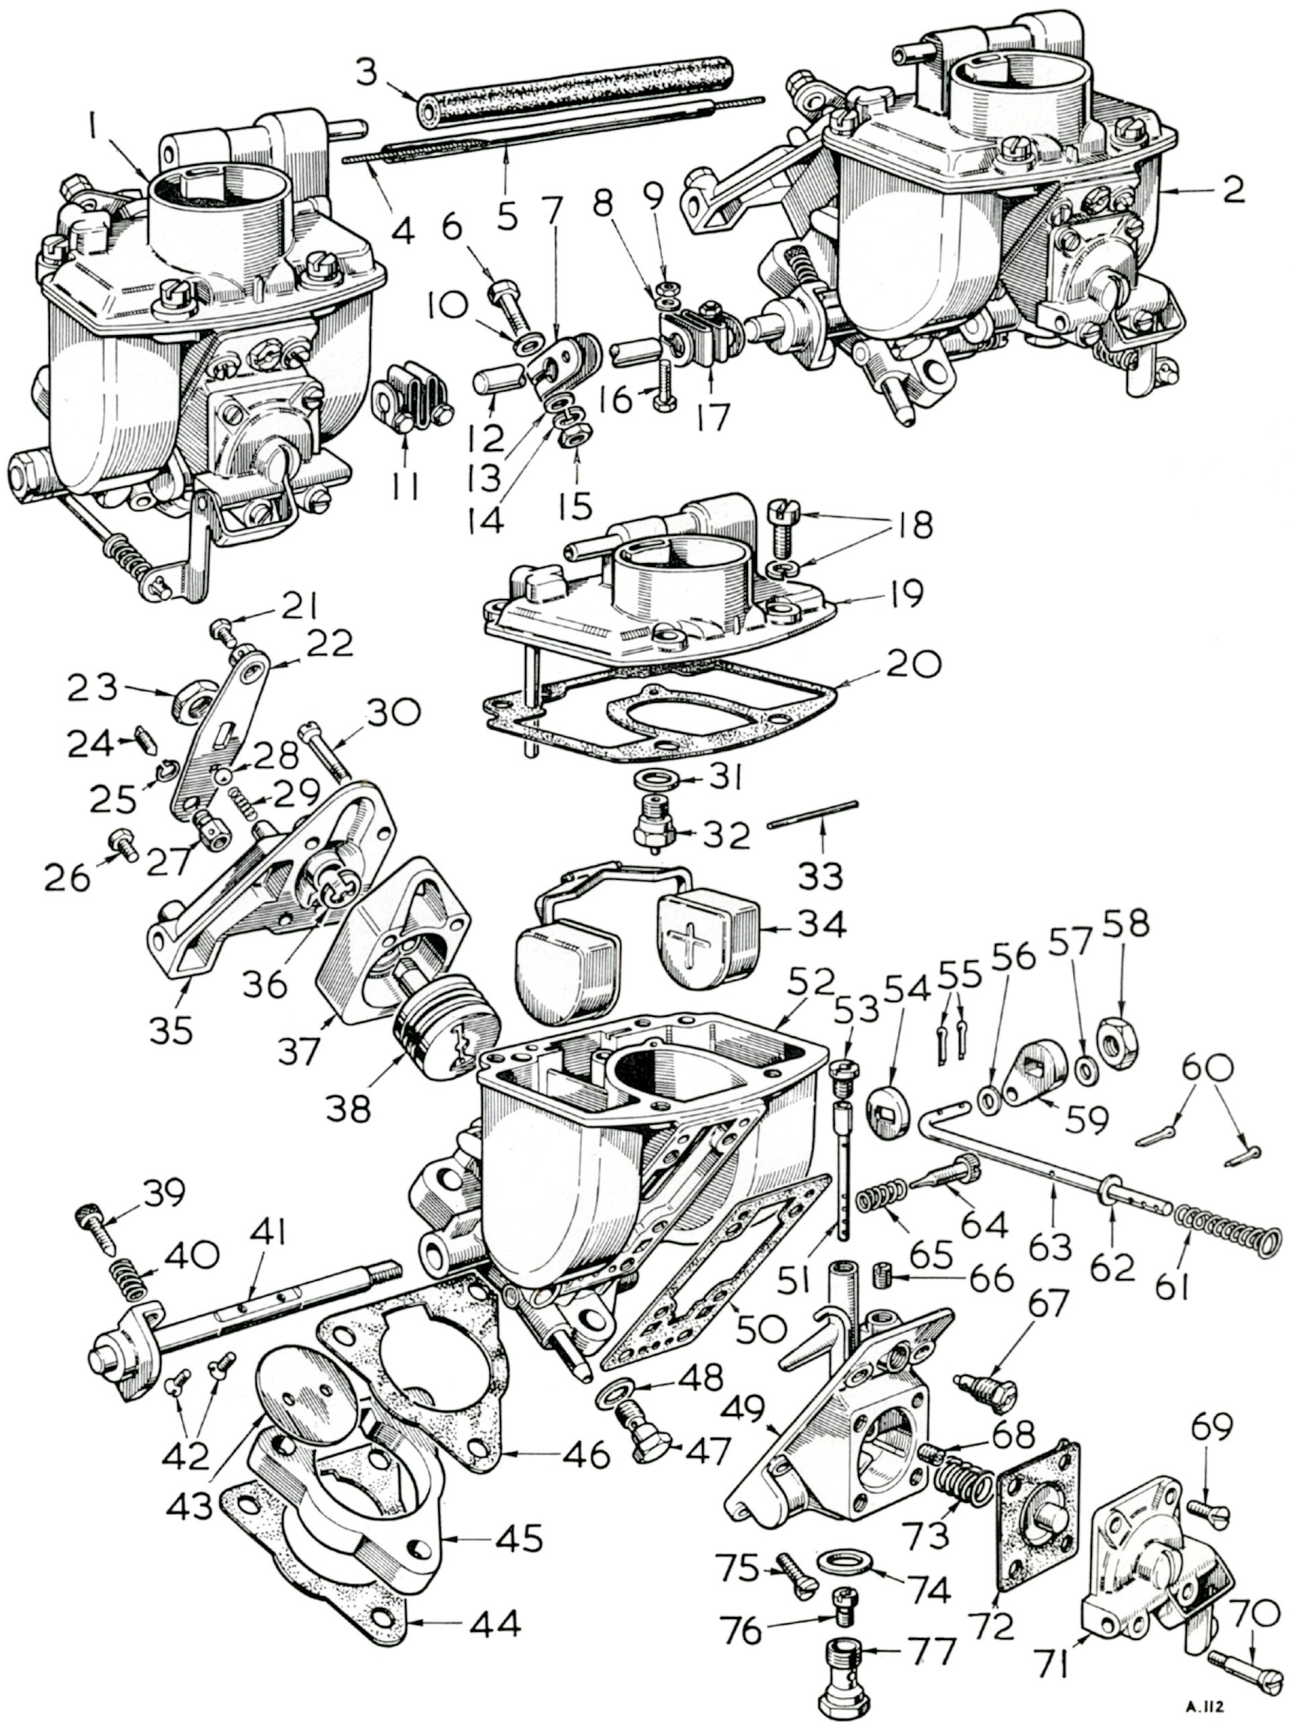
Vue éclatée du carburateur semi-inversé Solex B32 P1H
